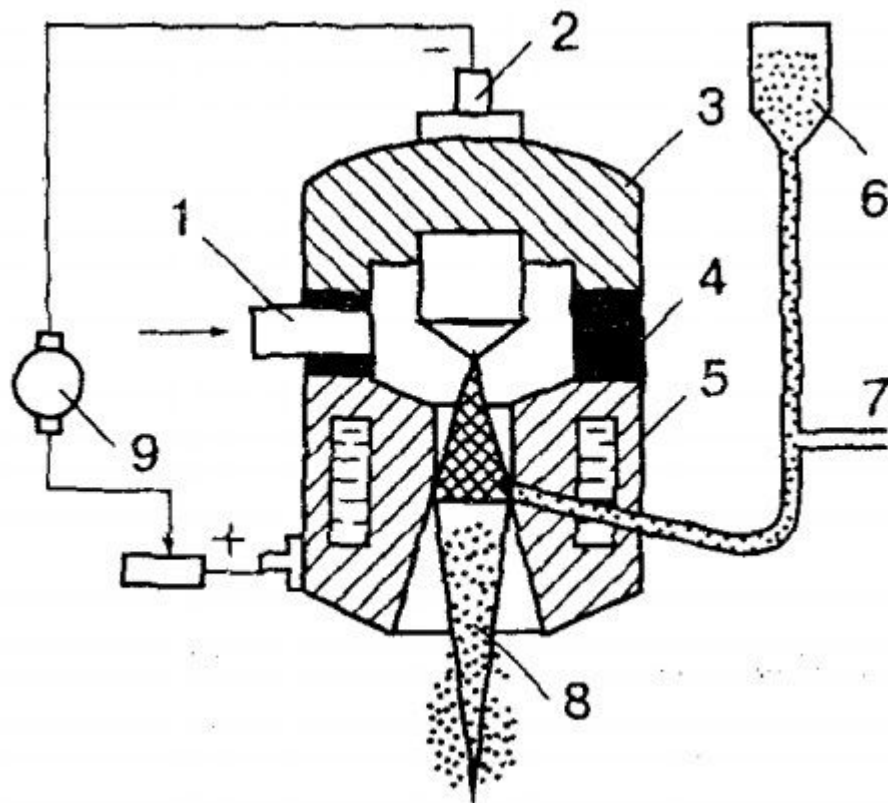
Принципиальная схема плазменного порошкового напыления: 1 - подвод плазмообразующего газа, 2 - катод плазмотрона, 3 - корпус катода, 4 - изолятор, 5 - корпус анода, 6 -порошковый питатель, 7 - подвод газа-носителя порошка, 8 - плазменная дуга, 9 - источник питания.
